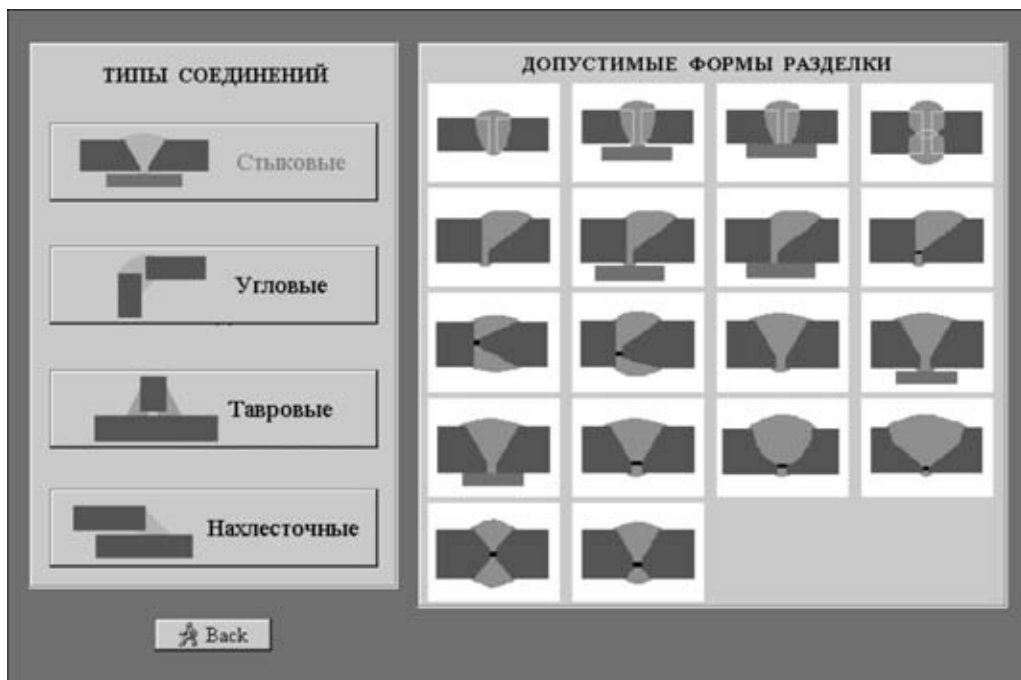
Выбор типа сварного соединения и формы разделки кромок при сварке легких сплавов
